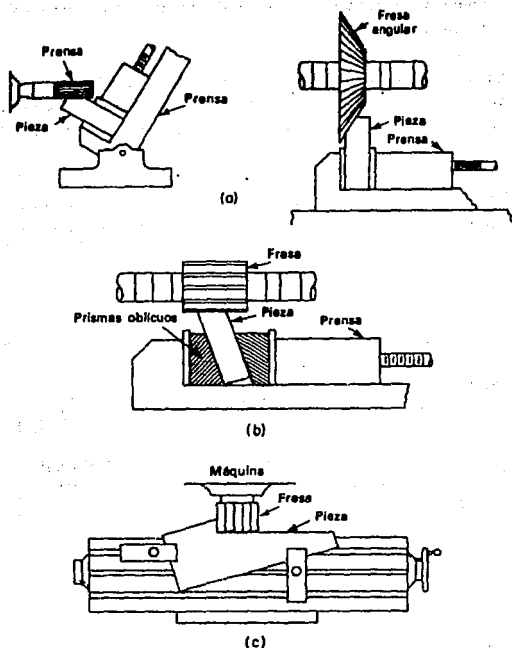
Fresado de chaflanes y superficies inclinadas
